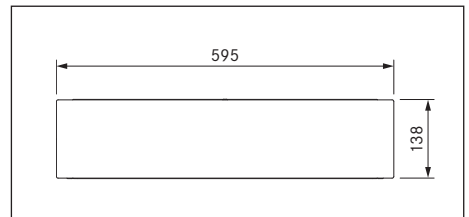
Dimensões do aparelho MSS140, vista frontal
